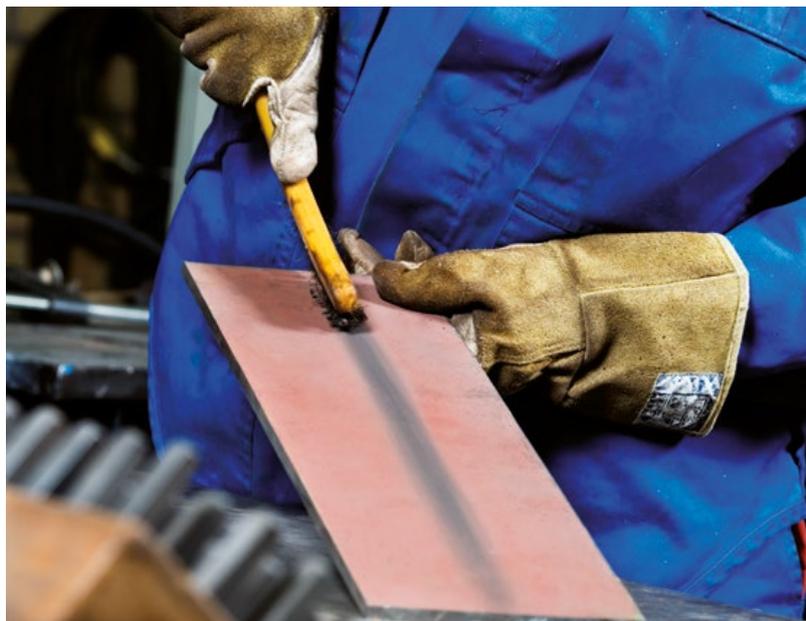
Beispiel für eine Rückschrittschweißtechnik
